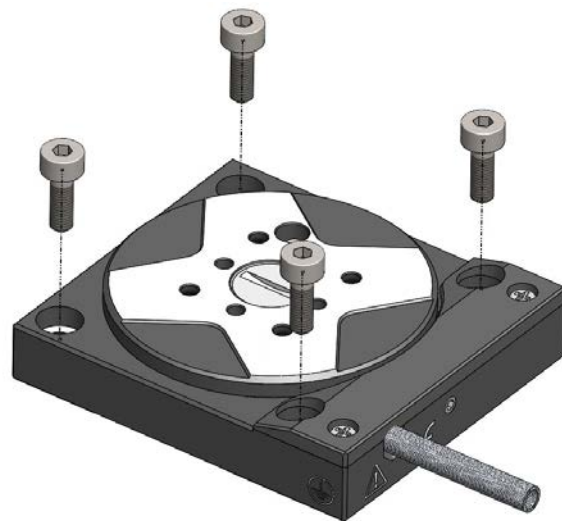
Oberseite des Q-632: Der Drehtisch wird mit vier Schrauben auf einer Unterlage befestigt: 4 Zylinderschrauben (für äußere Senkbohrungen)
